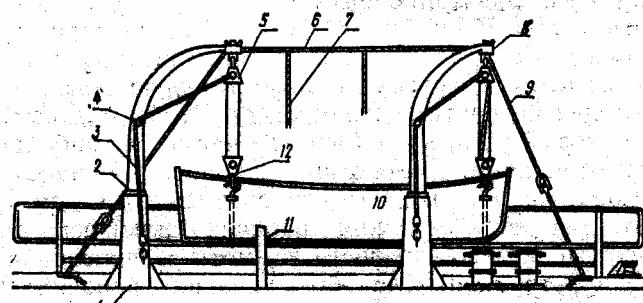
Шлюпочное устройство с поворотными шлюпбалками:
